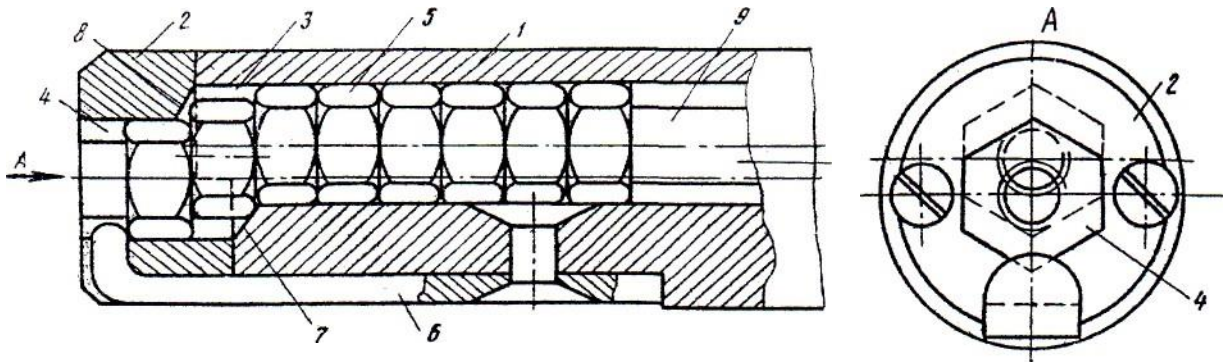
Магазинний пристрій до гайковерта: 1 - корпус; 2 - головка; 3 - канал; 4 - приймальний канал; 5 - гайки; 6 - пружний упор; 7, 8 - скоси; 9 - поршень.
